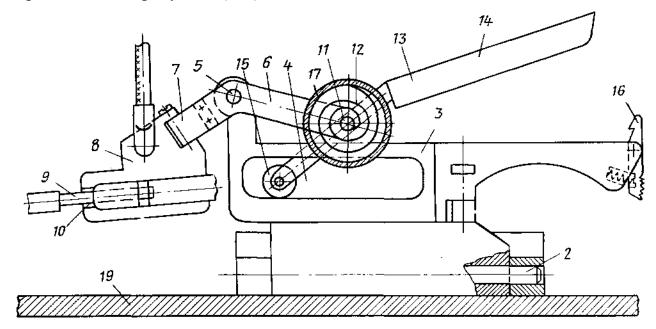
а - Устройство для сварки наклонным электродом вид сбоку
